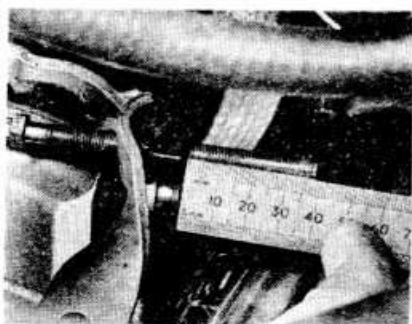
Измерение длины выступающего стержня с резьбой на конце троса выключения сцепления
